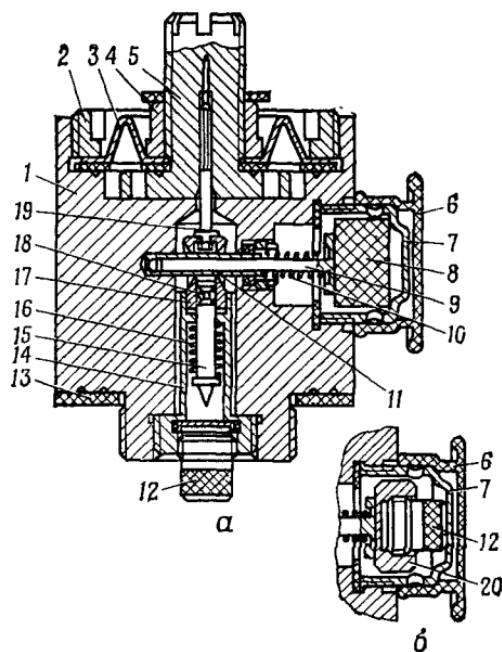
Взрыватель ВПДМ-1М (разрез):
